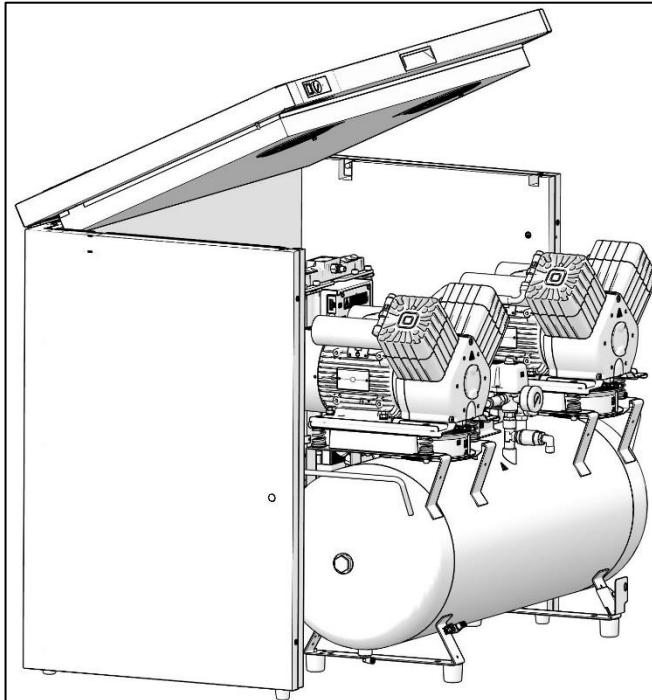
Positionierung des Kompressors für elektrische Anschlüsse
